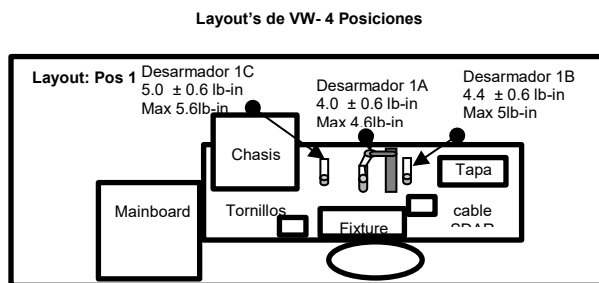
Presentación de partes de la línea final de VW, posición 1
